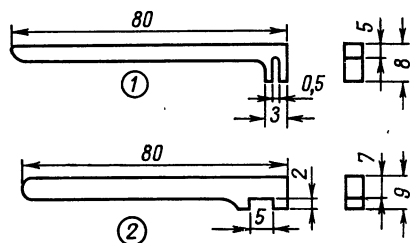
Приспособления для рихтовки контактов и отладки толкателей после сборки контактной системы (материал латунь).
